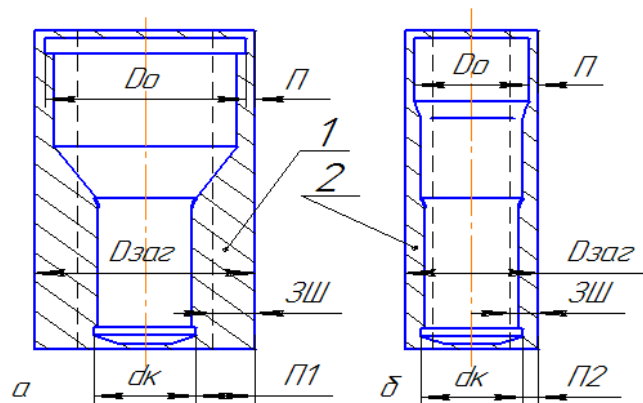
Залежність розмірів вихідної заготовки від особливостей конструкції пуансона. 3Ш – ширина здорової шкірки заготовки.
